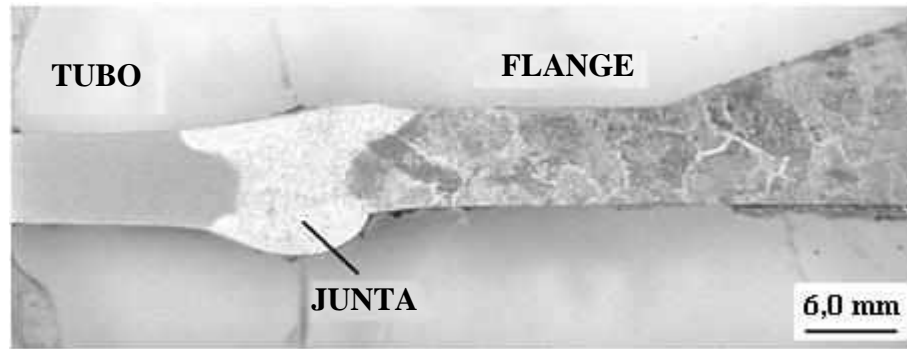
Macroestrutura do tubo, flange e metal de solda. Reagente ácido oxálico.
